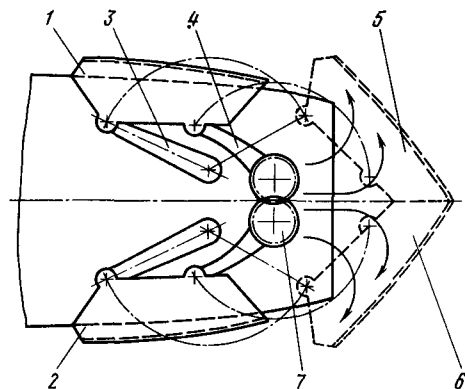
Схема реверсивного устройства с двумя створками; 1, 2 — створки; 3, 4 — рычаги; 5, 6 — положение створок на режиме реверсирования; 7 — зубчатое колесо
